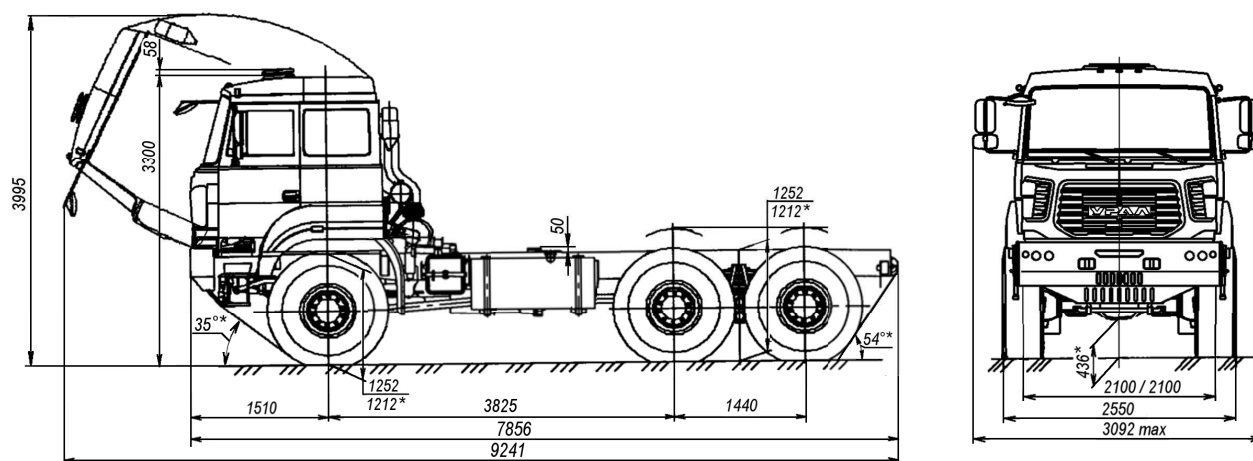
Размеры габаритные шасси Урал-6370-1151
